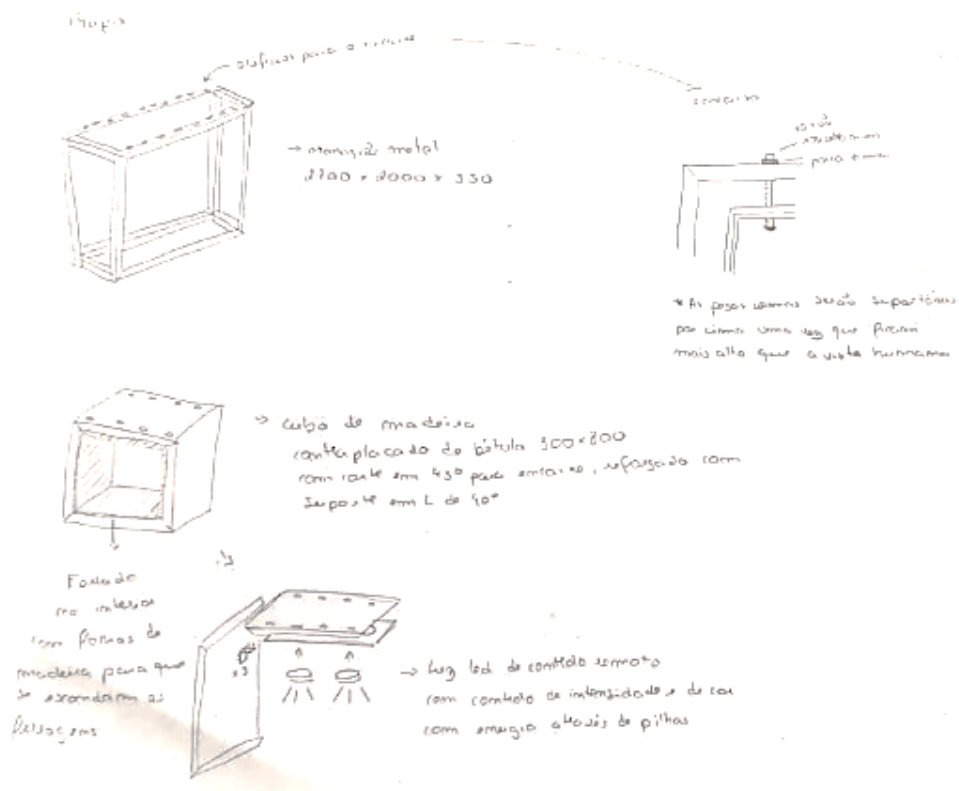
Desenhos Exploratórios do equipamento a desenvolver. Fonte: Autor.
